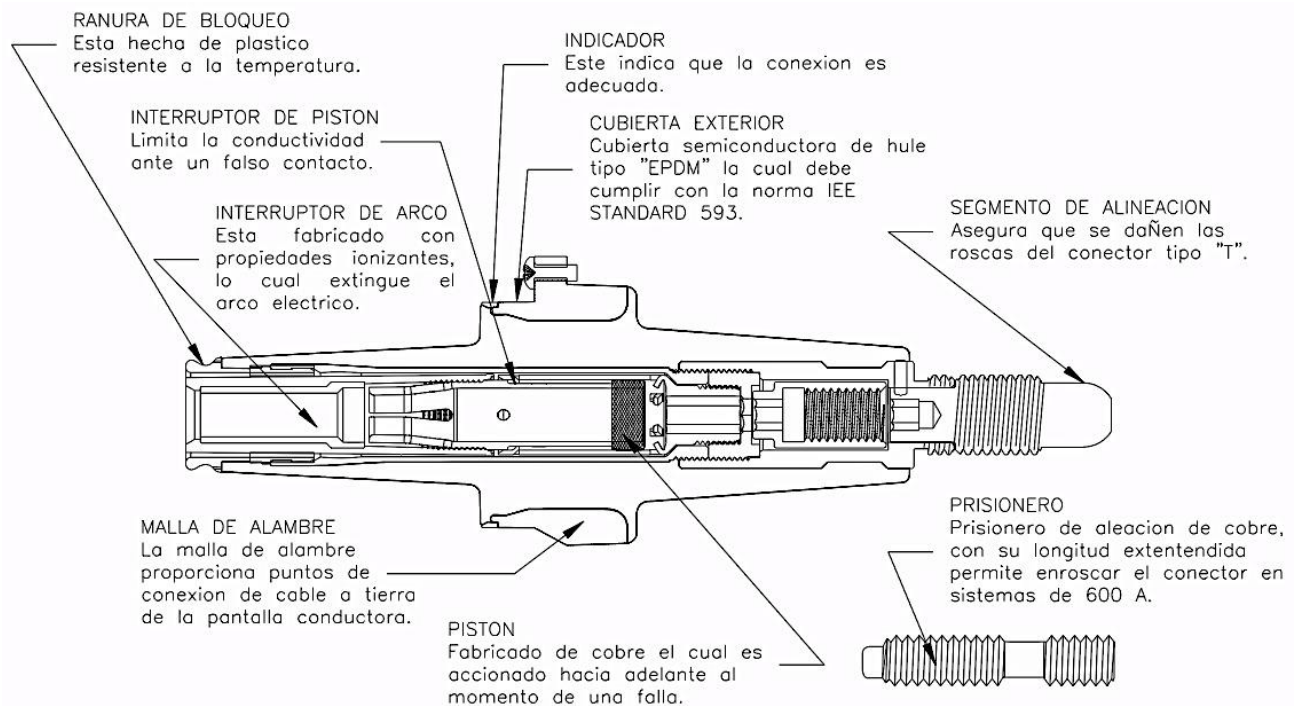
Partes de inserto tipo "BUSHING" 600 A, [12].
